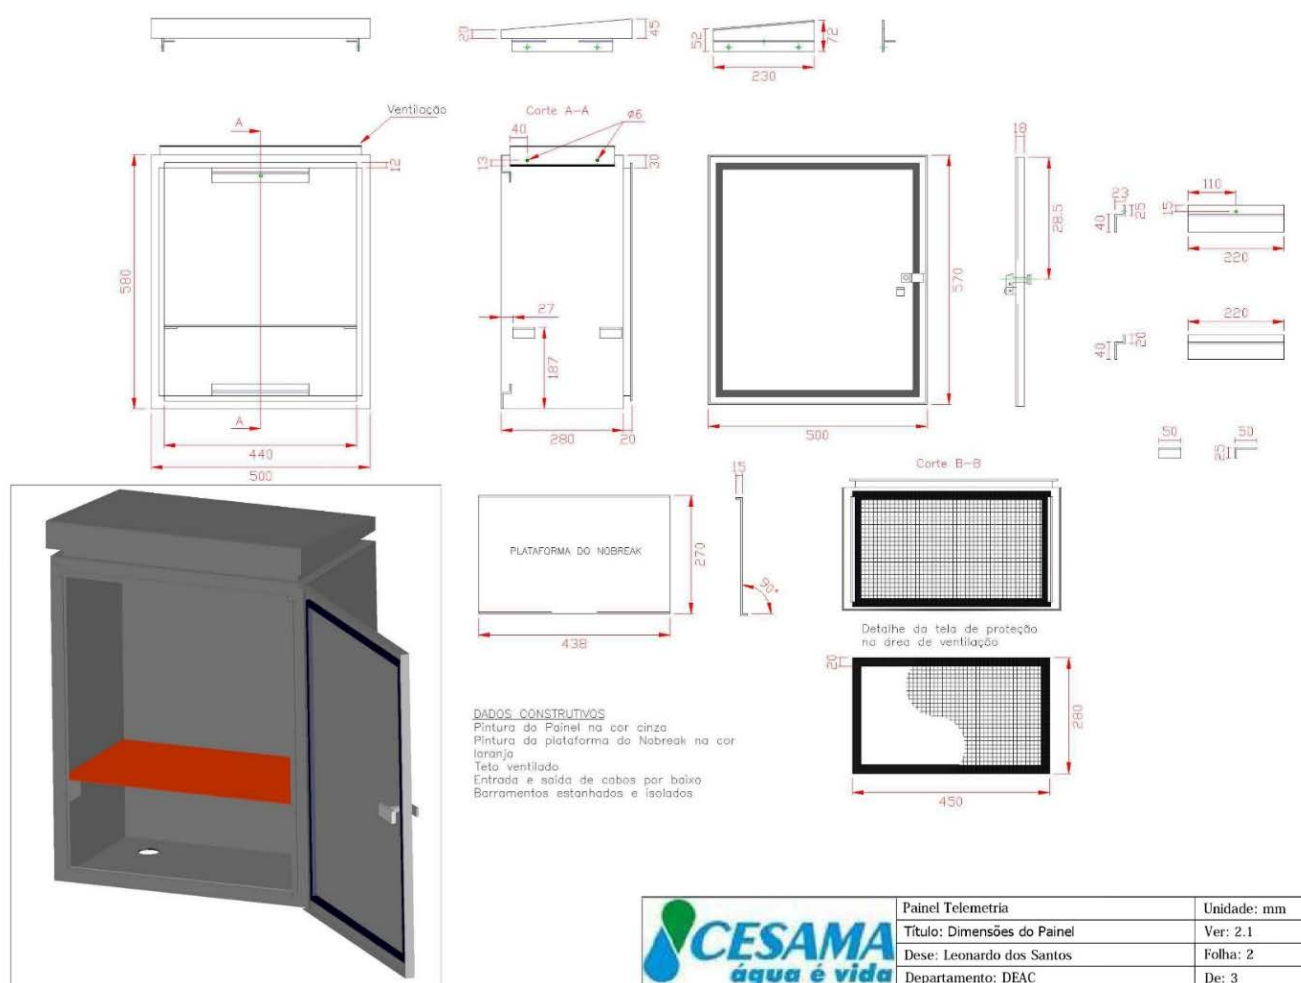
Detalhes construtivos painel de telemetria padrão CESAMA
